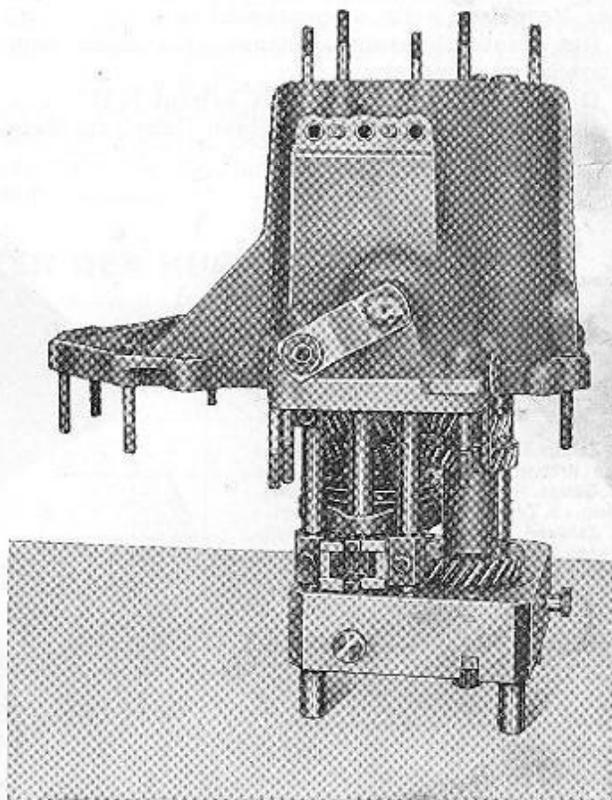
Montage des Getriebegehäuses auf das auf dem Werkzeug A. 70105 vormontierte Getriebe.
